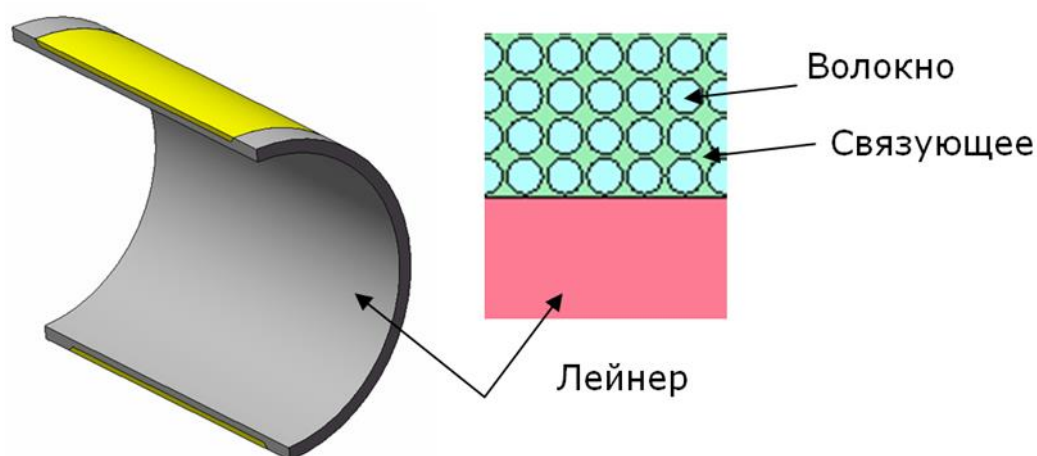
Расчетная схема металлокомпозитного малогабаритного корпуса
